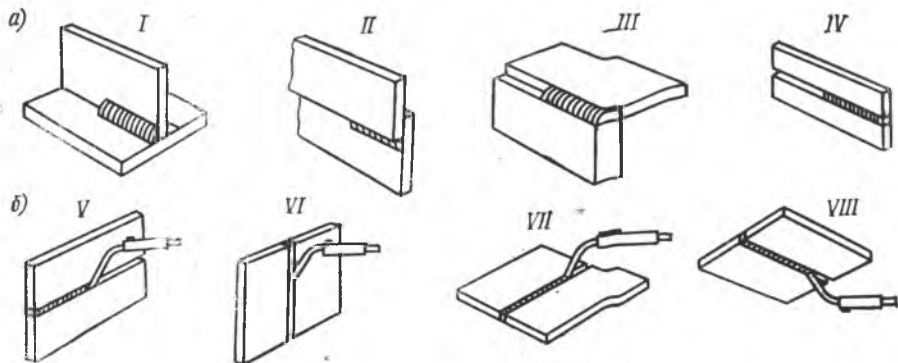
Виды сварных соединений и расположение сварных швов в пространстве
